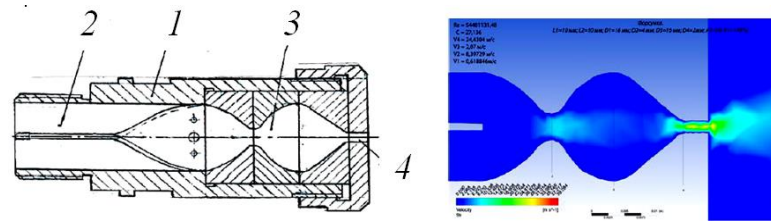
Схема кавітаційної форсунки та моделювання розподілу потоку миючої рідини: (а) 1 – корпус; 2 – камера закрутки струменю; 3 – камера Лавалля; 4 – сопло; (б) – оцінка розповсюдження кавітаційного поля миючої рідини
